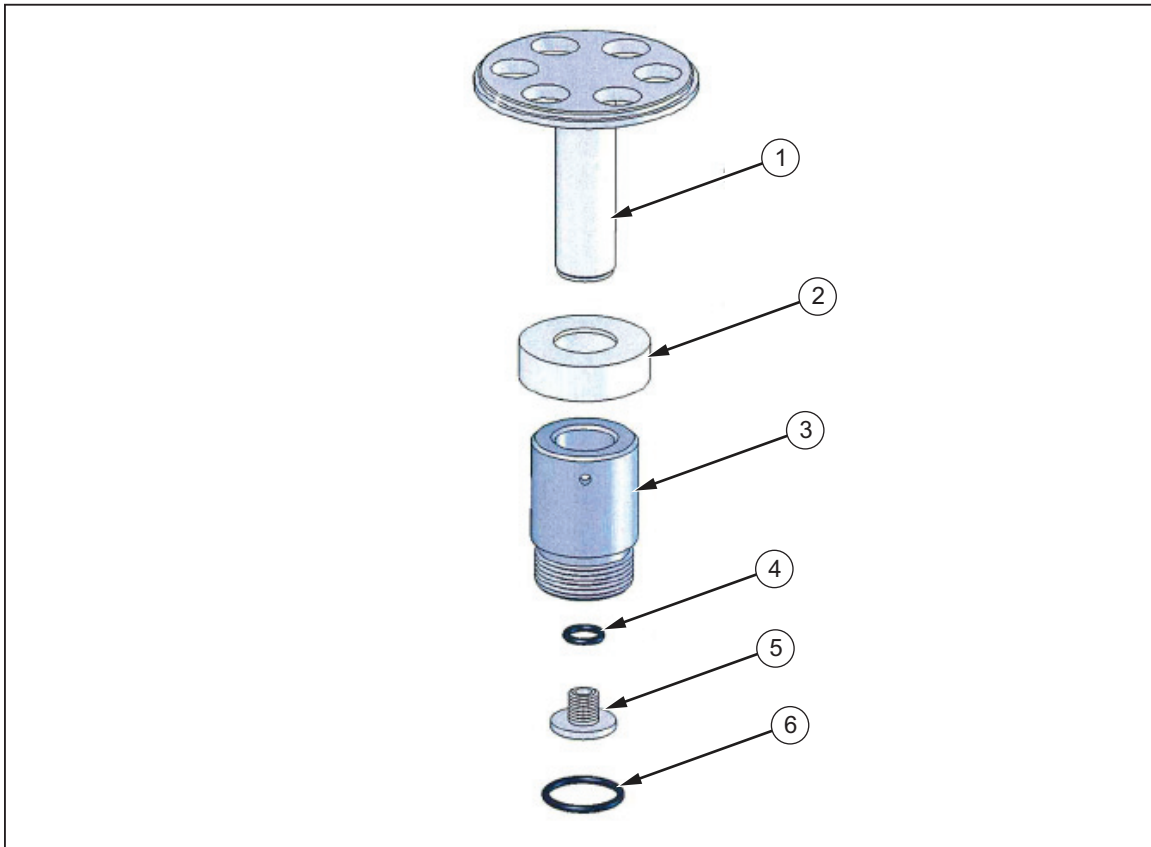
Сборочный чертеж поршневой пары - 16 мм
